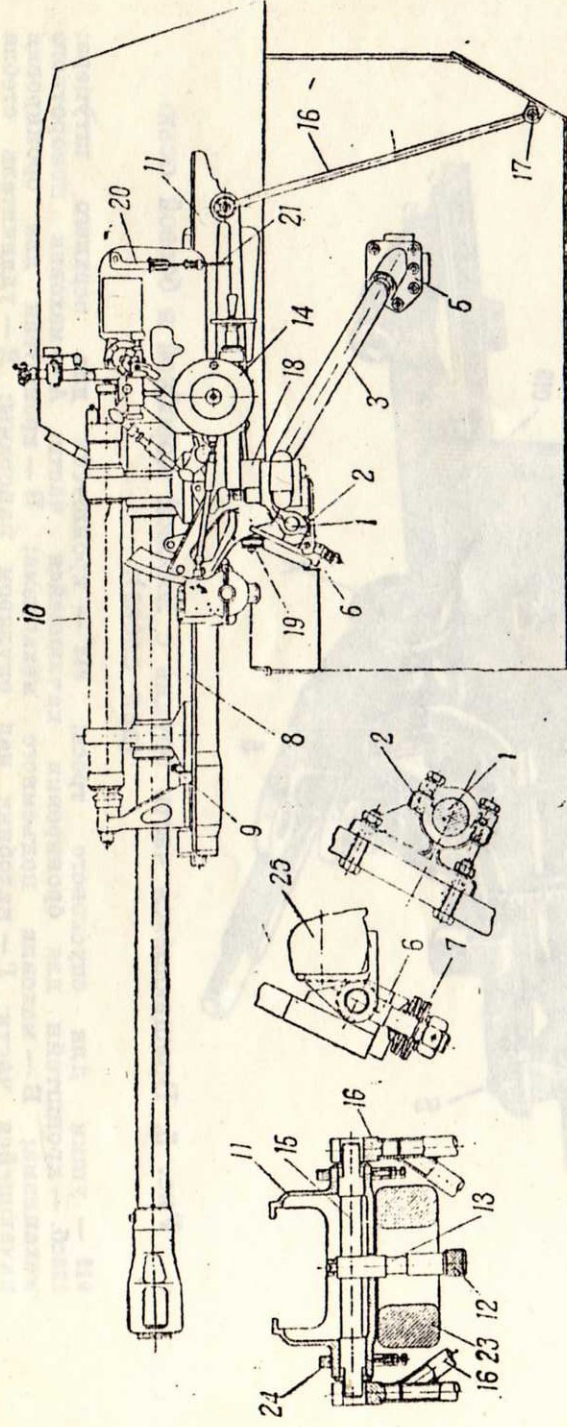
Установка пушки по-походному (вид слева) (номера произвольные):
